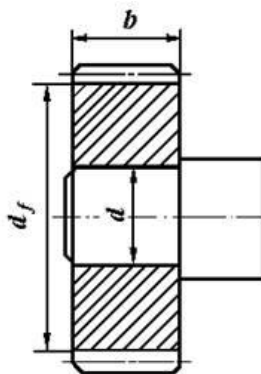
Цилиндрическое соединение вала и шестерни с натягом
